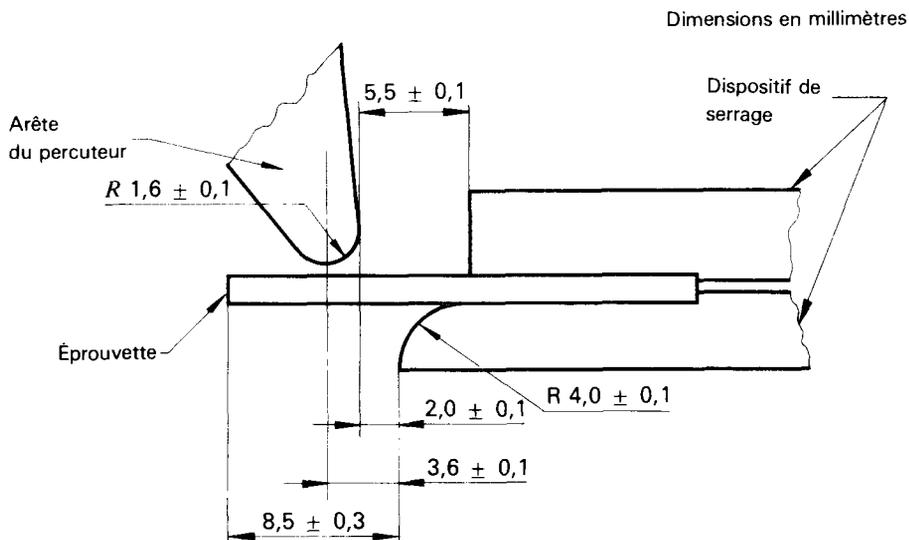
Dimensions de l'arête du percuteur et du dispositif de serrage (Mise en position d'une éprouvette non entaillée)
